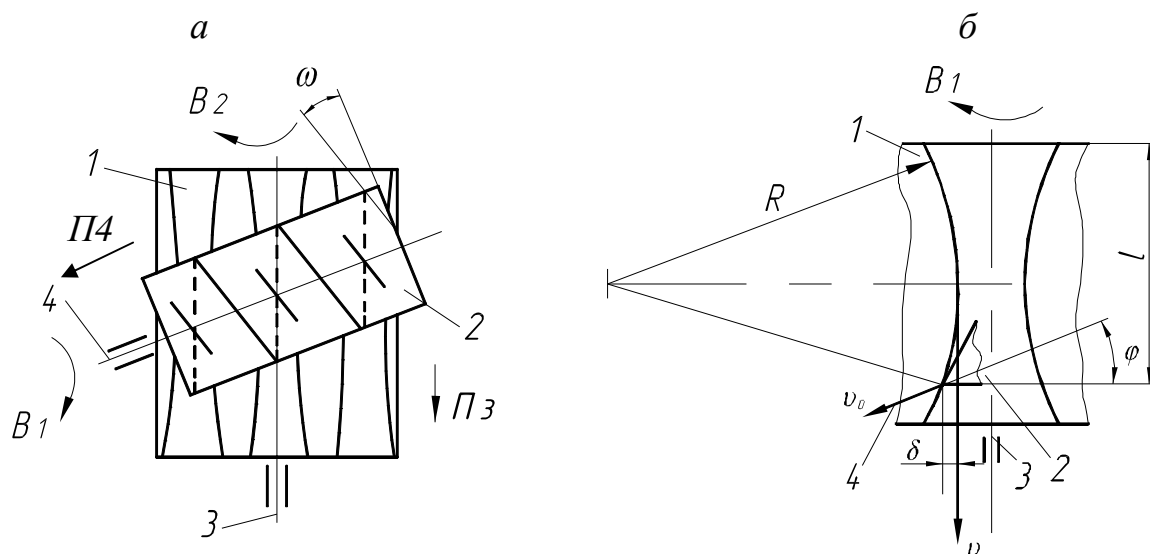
Схемы диагонального зубофрезерования колес с бочкообразными зубьями: а – кинематическая схема обработки; б – кинематика образования бочкообразной формы зубьев
